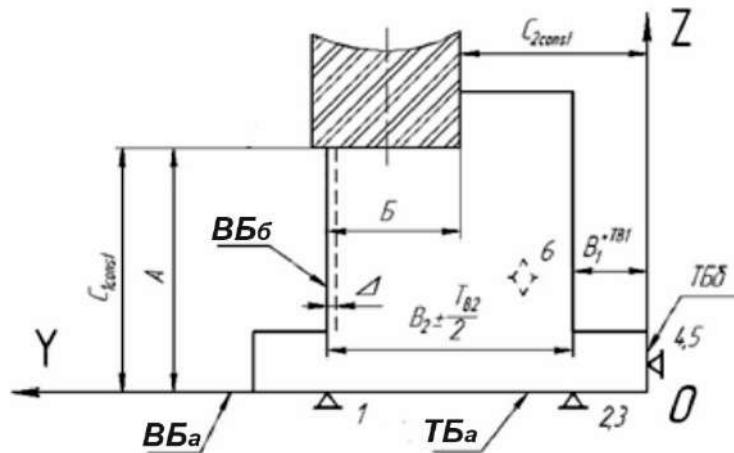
Встановлення деталі під час фрезерування.
